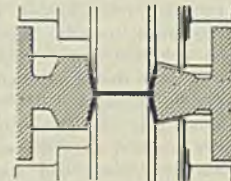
Erstes Gerüst, Walzen geschlossen.
